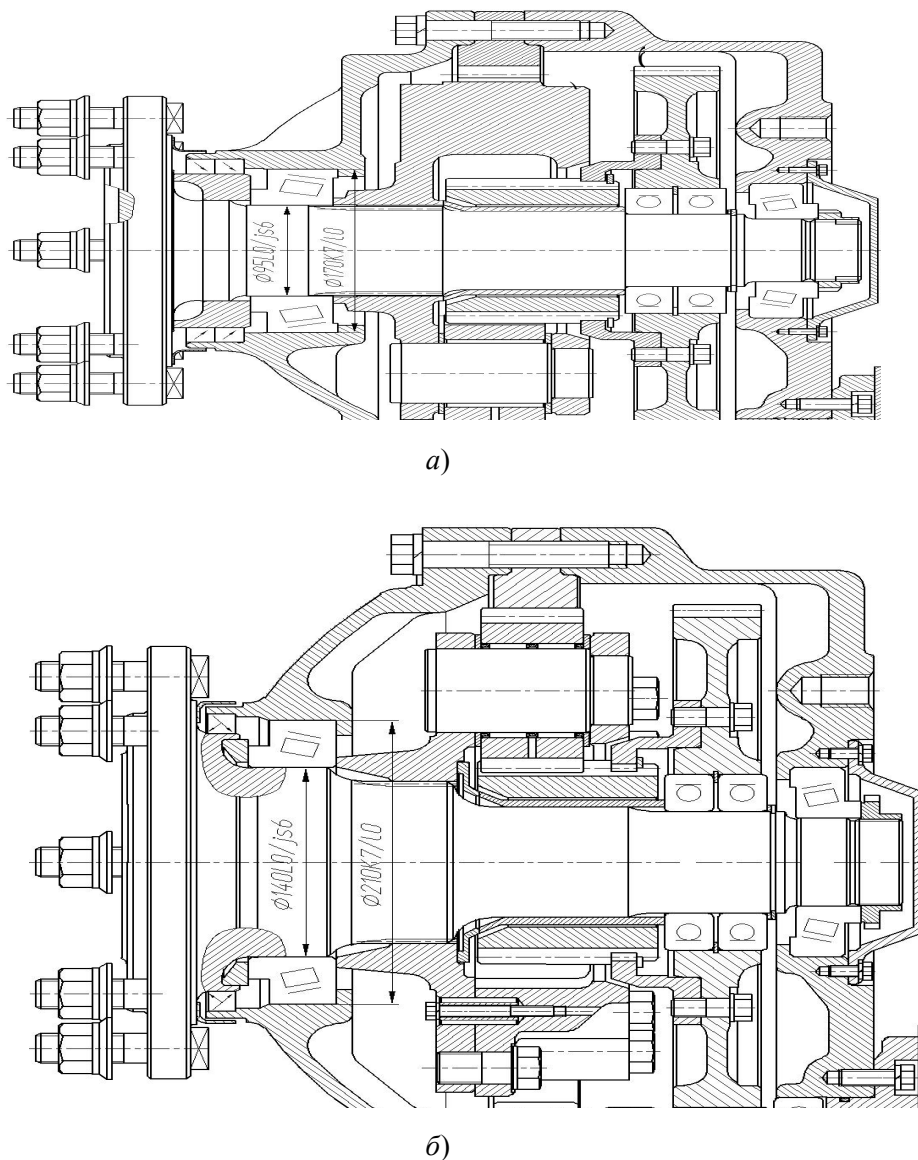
Бортовой редуктор зерноуборочного комбайна КЗС-10К:
